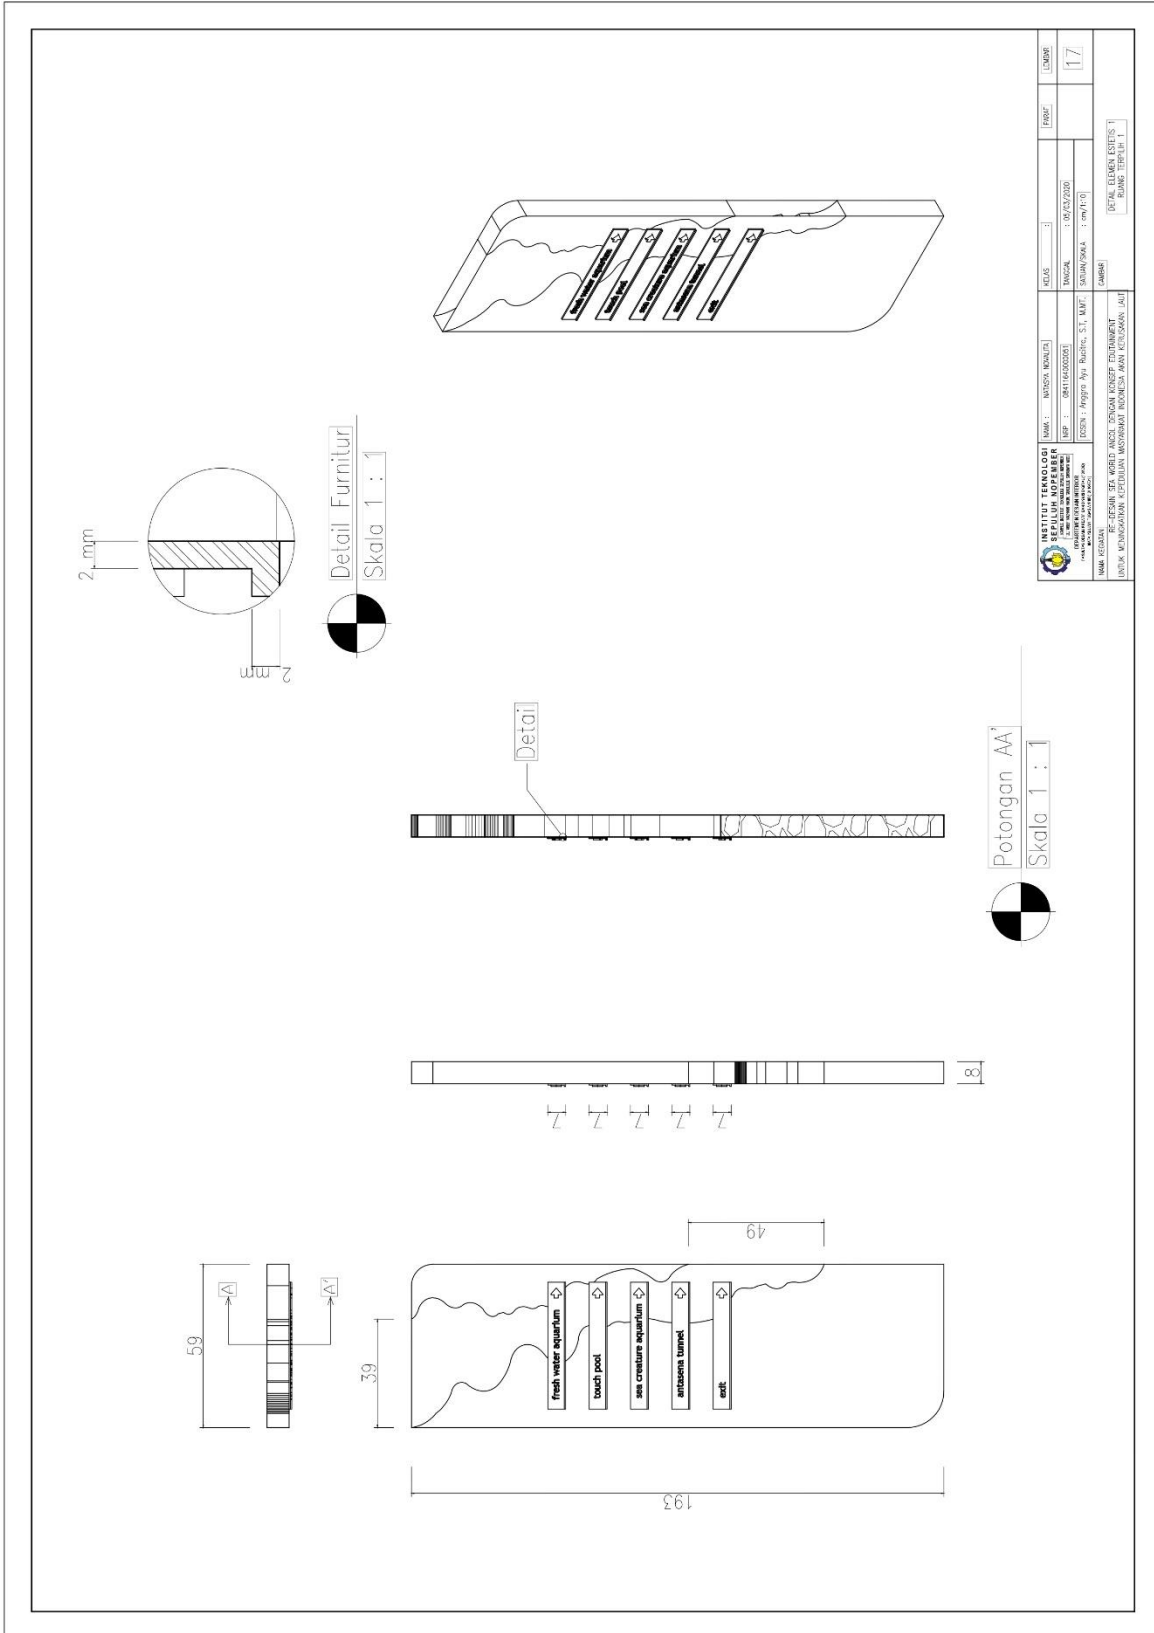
Ruang Terpilih 1 (Introduction Room)
